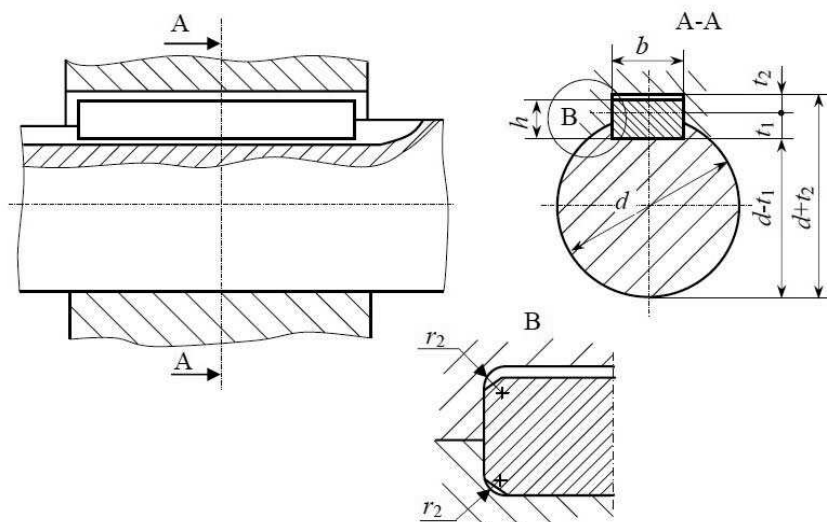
Dimensiunile asamblării cu pană paralelă
